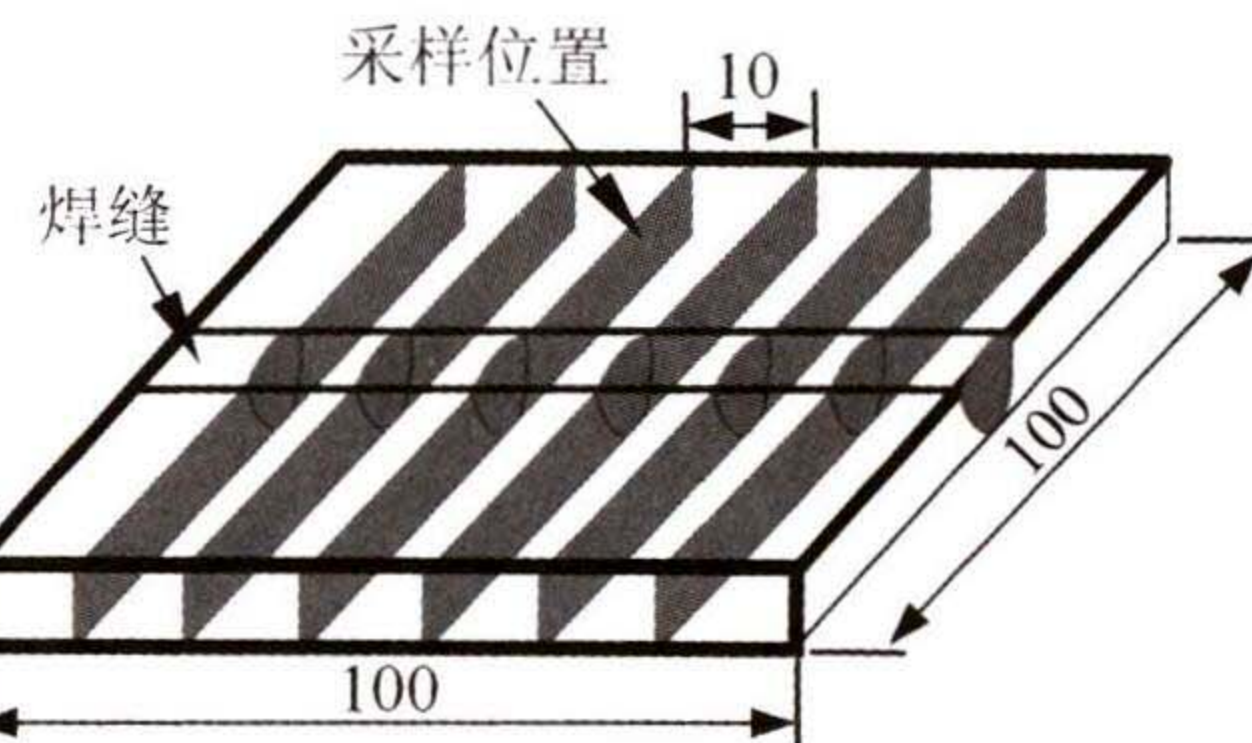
焊缝横截面气孔采样示意图(mm)
